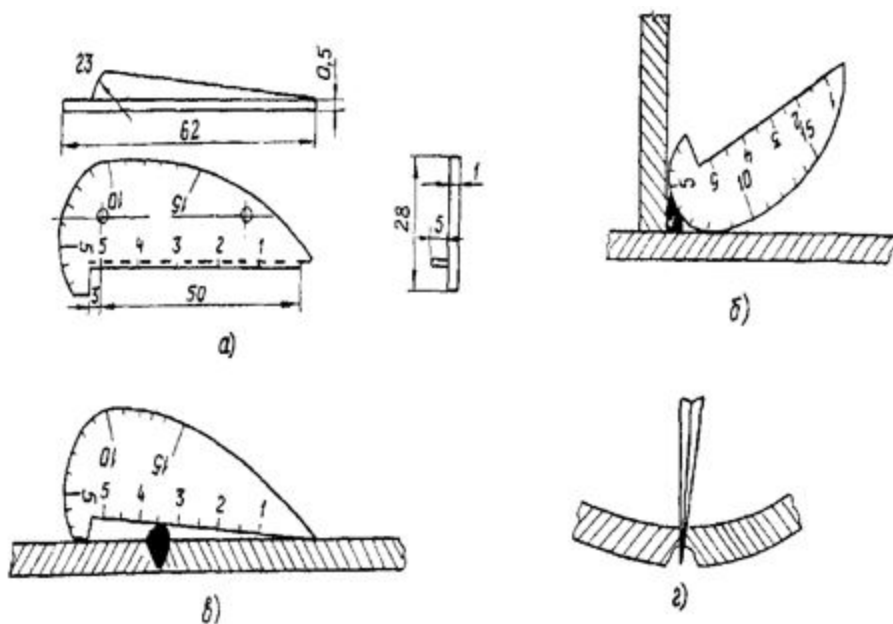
Шаблон для измерения габаритных размеров сварных соединений:
